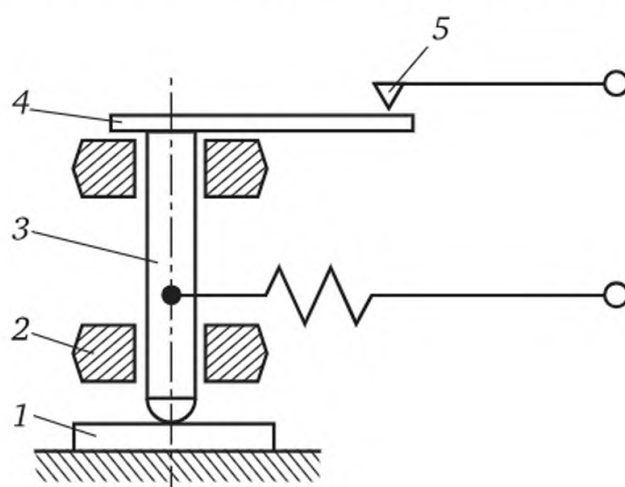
Схема одноконтактного преобразователя перемещений
